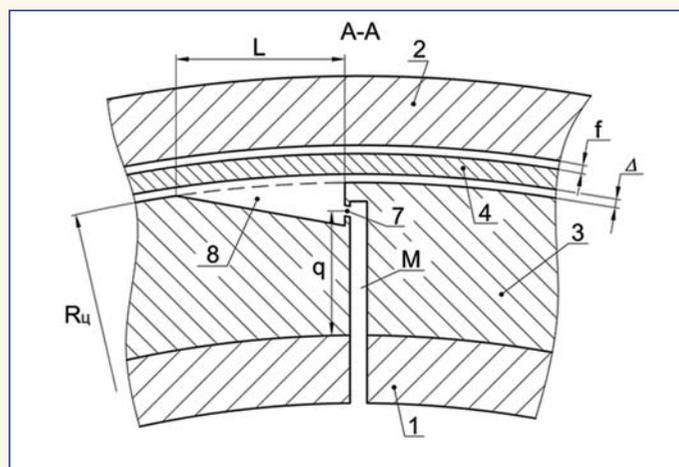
Схема подачи масла в клиновидный зазор подшипника. Вид А на рис. 3
